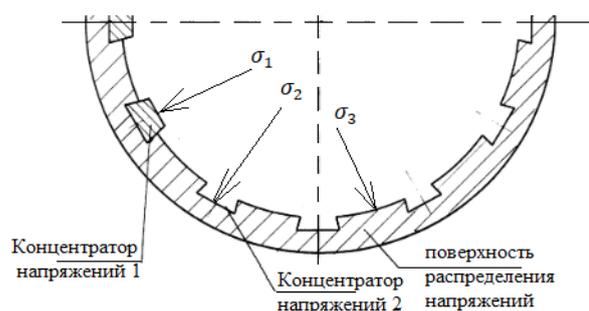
Концентраторы напряжений и опасные сечения внутри конструкций металлических труб (половина поперечного сечения трубы)
